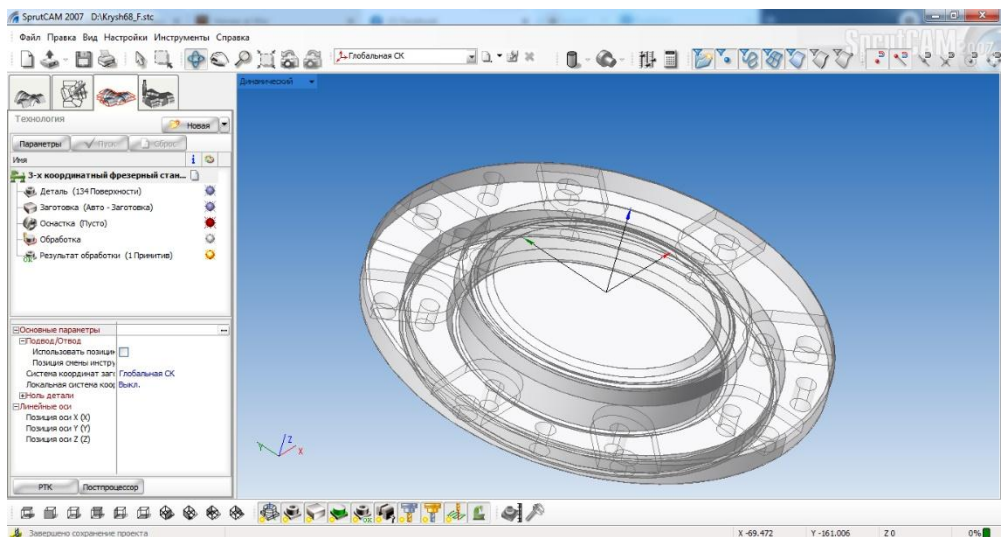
Імпорт 3D-моделей деталі та заготовки для фрезерної обробки
